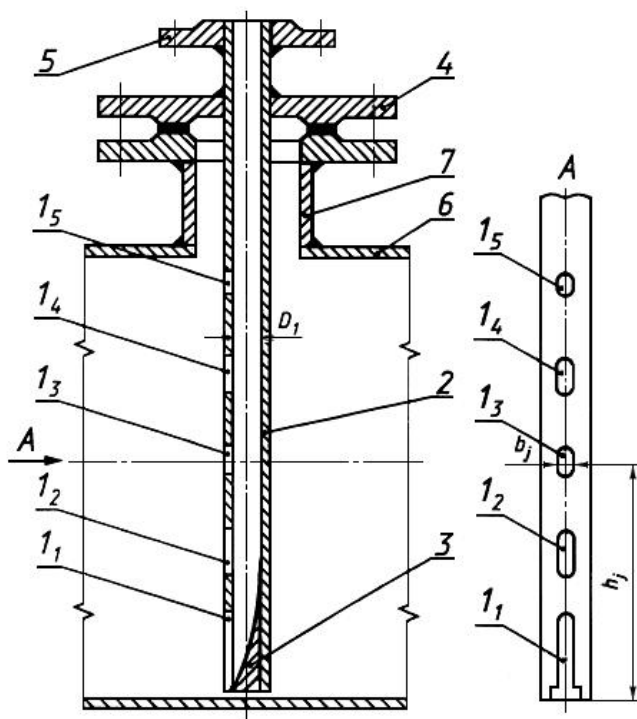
Пробозаборное устройство щелевого типа с пятью отверстиями: 1 - отверстия; 2 - трубка; 3 - стабилизатор; 4 - крышка; 5 - штуцер; 6 - трубопровод; 7 - монтажный патрубок
